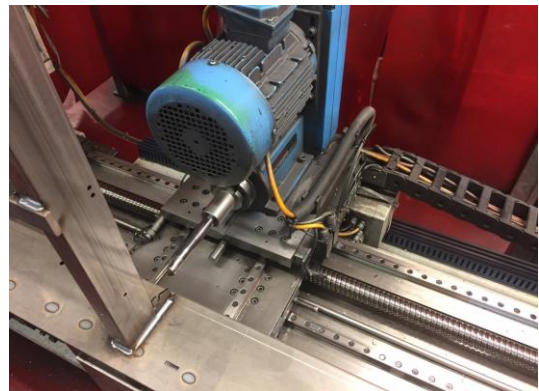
Alle Bohr und Fräseinheiten sind Suhner Einheiten. Unten Bohren Übersetzung 2/1 4 poliger Motor macht 1400 Umdrehungen; Spindel oben 2800 mit FU 80% = 50 Hz. Kann auf 60 Hz erhöht werden mit dem % Schalter am Panel
